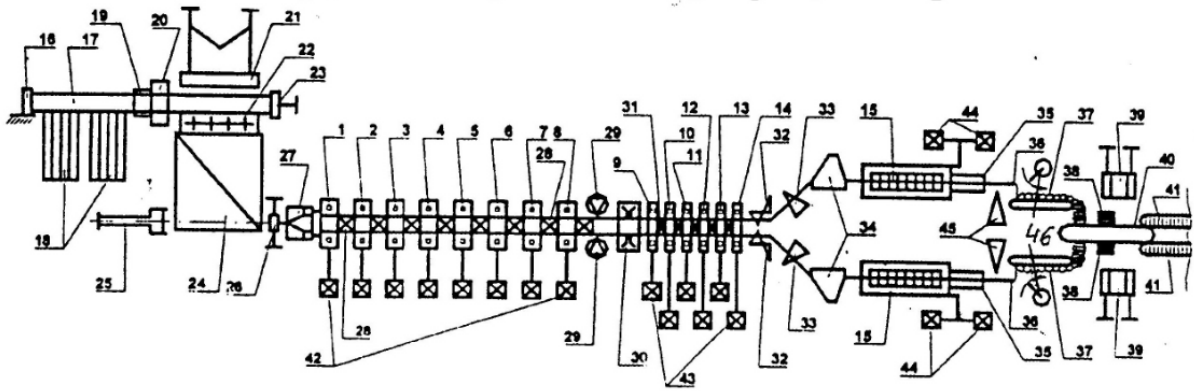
Схема розташування обладнання БДС 150: 1 – 8 – чорнова, 9-14 – проміжня і 15 блок - чистової групи клітей; 16 – обмежник; 17 – подаючий рольганг; 18 – завантажувальні столи; 19 – вагівниця; 20 – шлепербракованих заготовок; 21 – заштовхувач; 22 – решітка; 23 – обмежник; 24 – нагрівальна піч; 25 – виштовхувач; 26 – прийомні ролики; 27 – трайб-апарат; 28 – кантуючиролики; 29,32,33,45 – ножиці; 30 – устрій скидання обрізків; 31 – кантуючи ролики; 34 – петльовики; 35 – устрій прискороного охолодження дроту; 36 – утворювачі витків; 37 - транспортери витків; 38 – дорн; 39 – обтискний прес; 40 – конвеєр; 41 – конвеєр; 42,43,44 – електродвигуни клітей і блоків; 46 – вентилятори.
